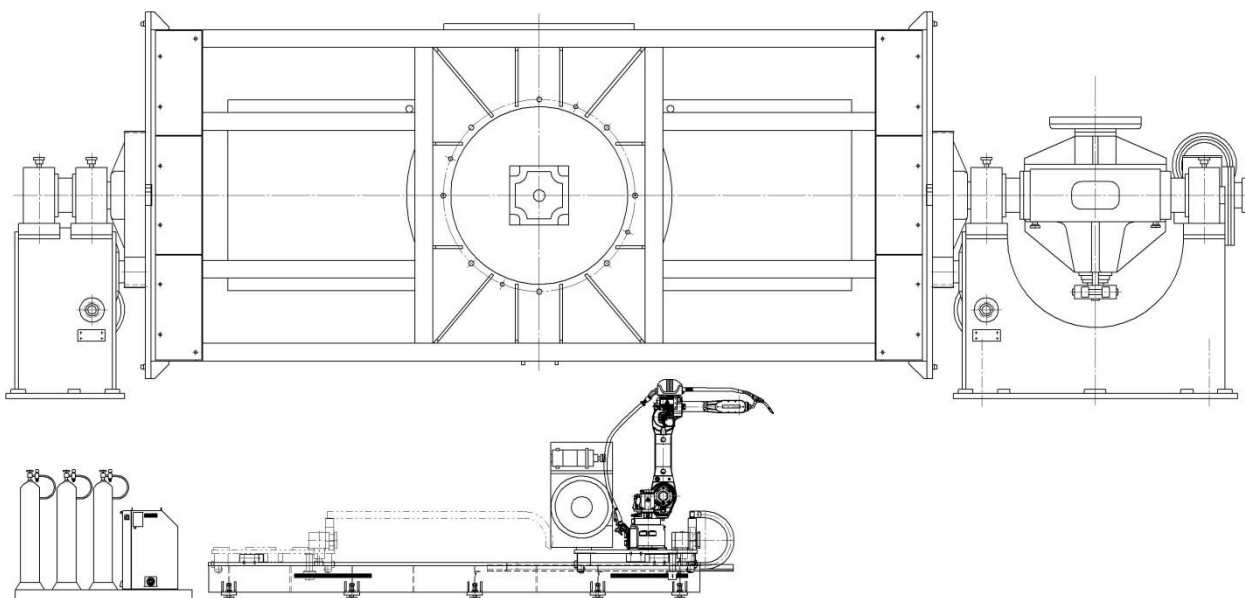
Концепция построения роботизированной сварки
